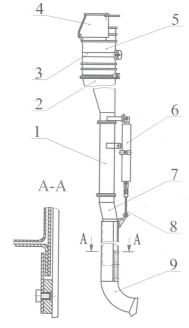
Установка отдува буровой мелочи: 1 – воздуховод; 2 – диффузор; 3 – хомут; 4 – кожух; 5 – вентилятор; 6 – цилиндр; 7, 9 – воздуховод; 8 – трос
